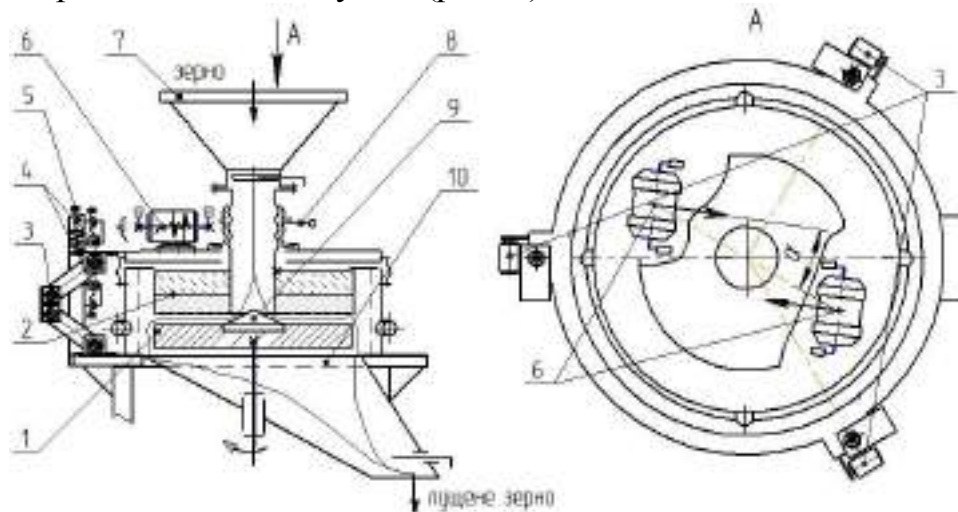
Принципова схема дискової лущильної машини з вібраційним диском: 1 – обертальний диск; 2 – вібраційний диск; 3 – пружна опора; 4 – обмежувач коливань; 5 – натяжний механізм; 6 – вібратор; 7 – бункер; 8 – механізм регулювання зазору; 9 – розподільча тарілка; 10 – основа
